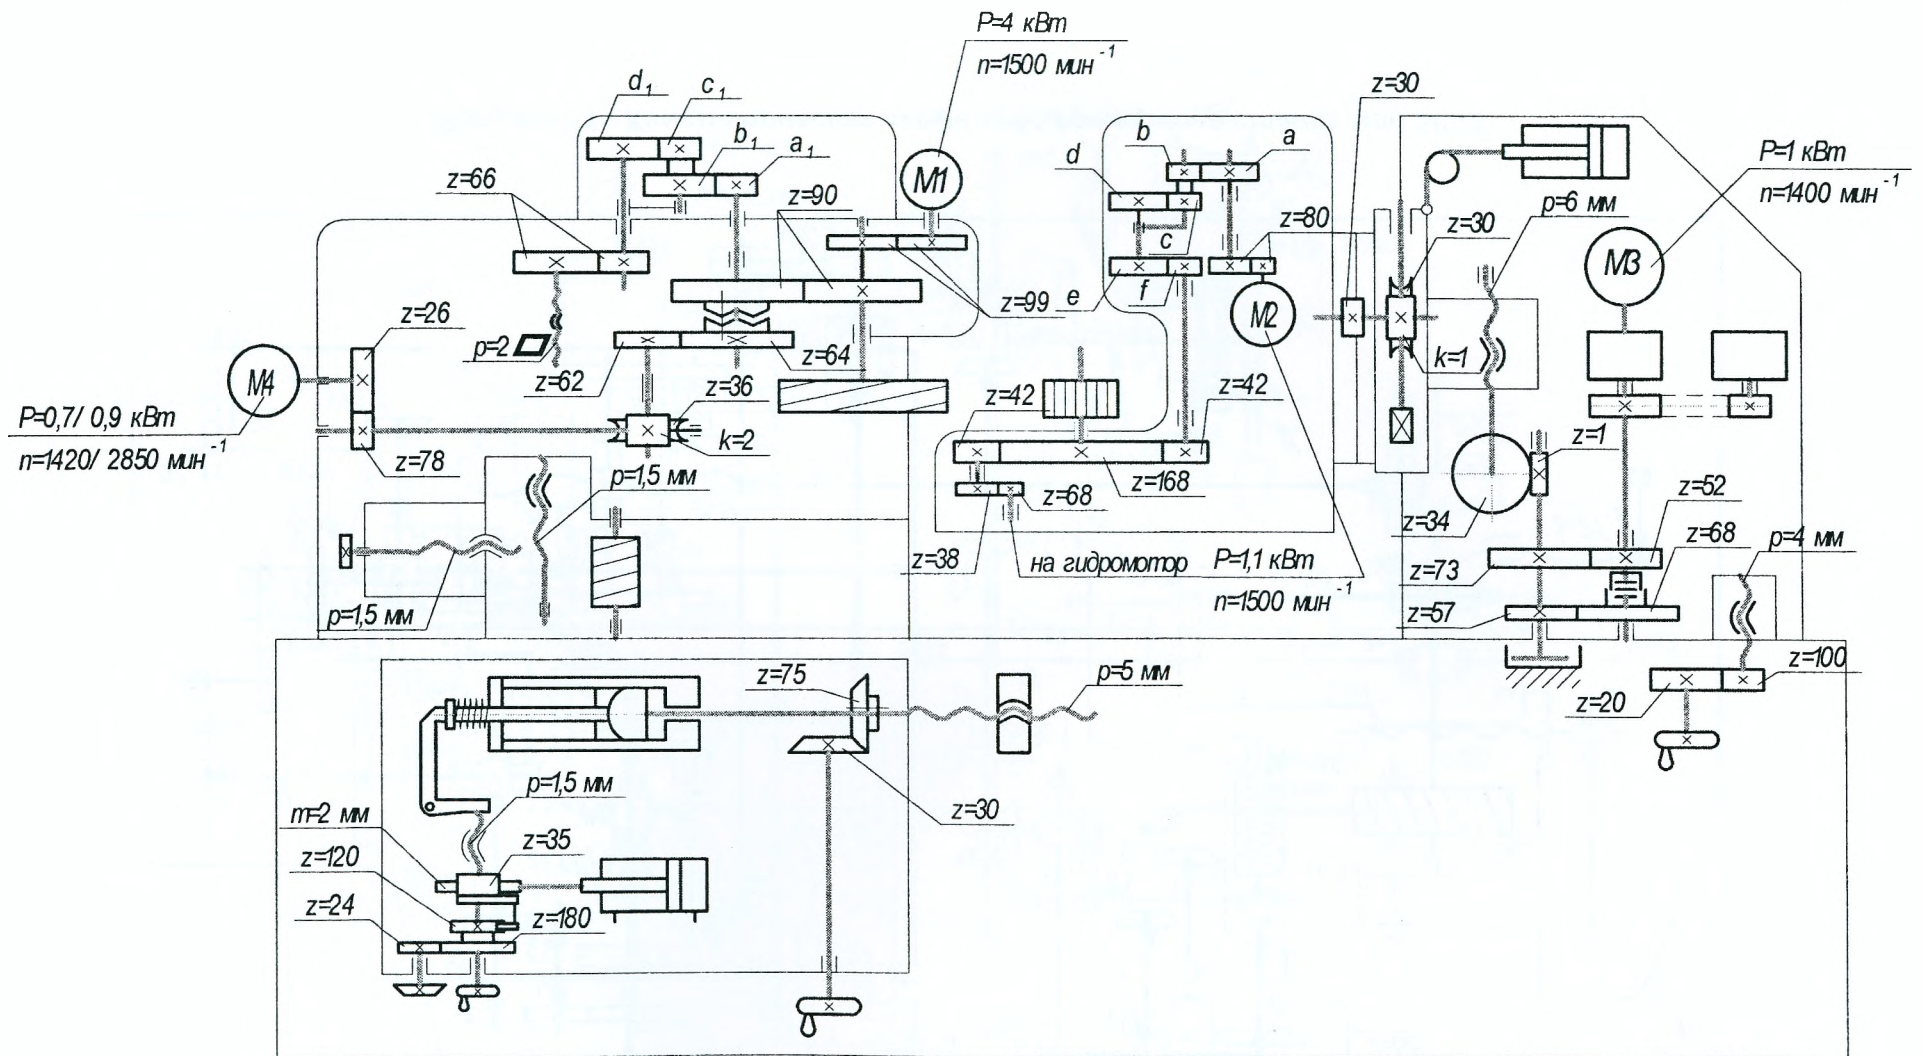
Кинематическая схема зубошлифовального станка мод.5B833
